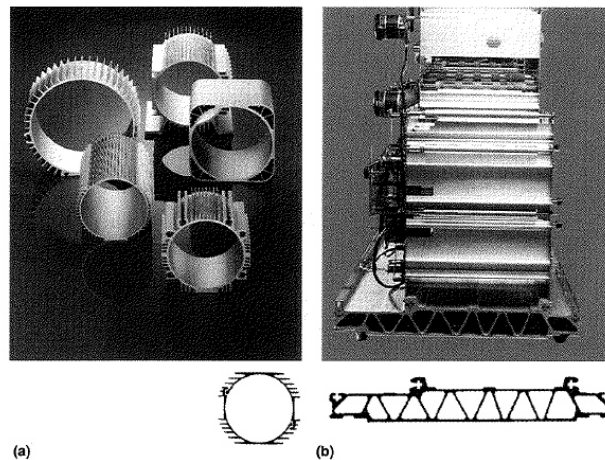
Extrusiones de aluminio para carcasas de motores de aluminio.
